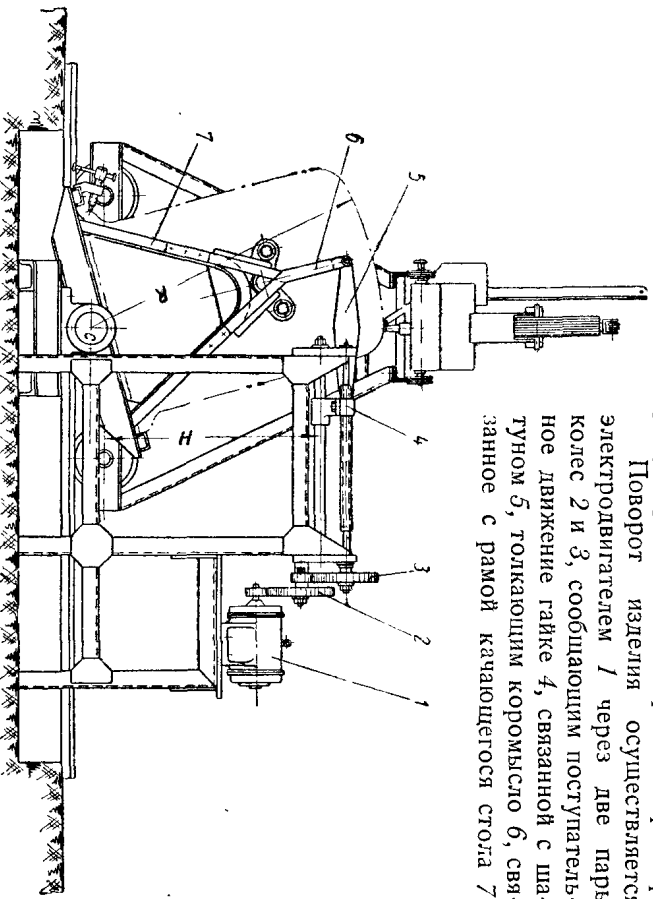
Схема установки с вращателем станочного типа для сварки криволинейных швов.
